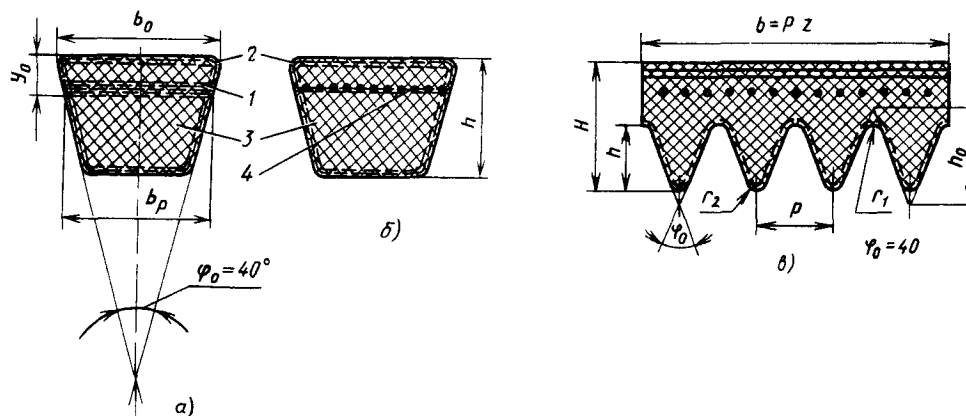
Клиновые и поликлиновые ремни: 1 – слой кордоткани; 2 – слой прорезиненной ткани (обертка); 3 – резина; 4 – кордошнур
